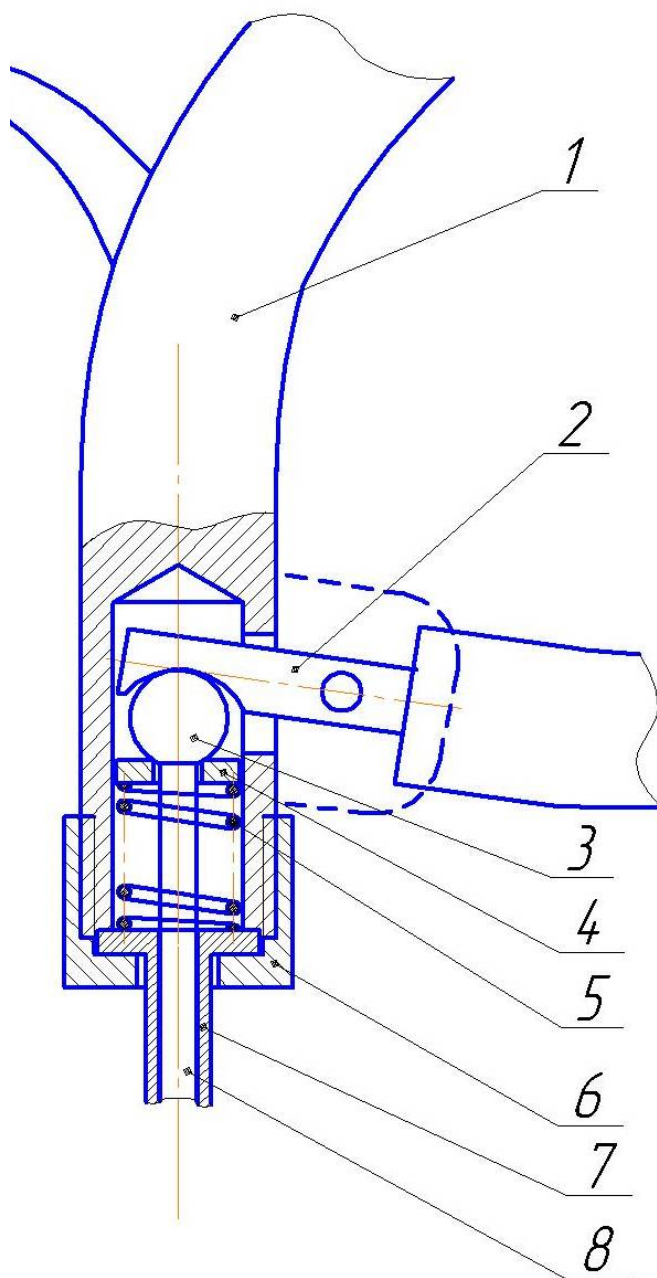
Креслення рукоятки з механізмом привода ножиць
